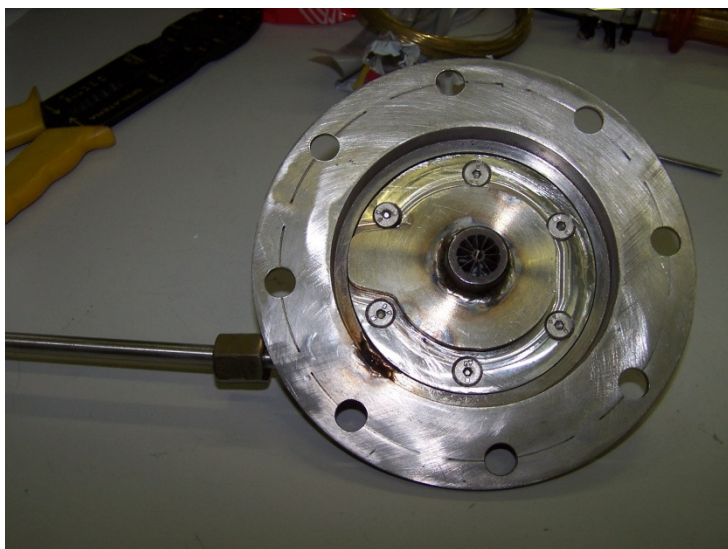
Assemblaggio testa del reattore – particolare assemblaggio parte 1 (supporto) e parte 2 (camera di miscelamento)
